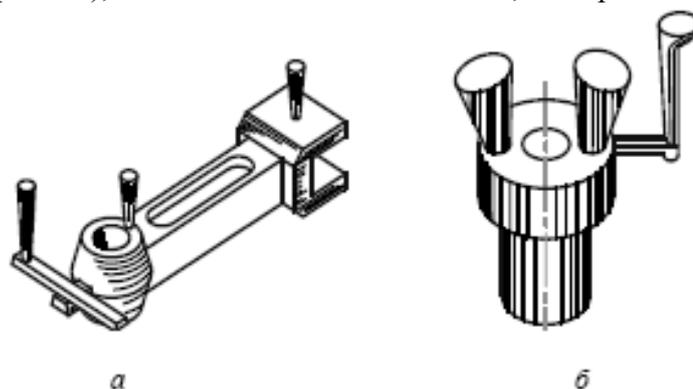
Отливки с литниковой системой: а – чугунная отливка рычага; б – отливка стальной втулки.
